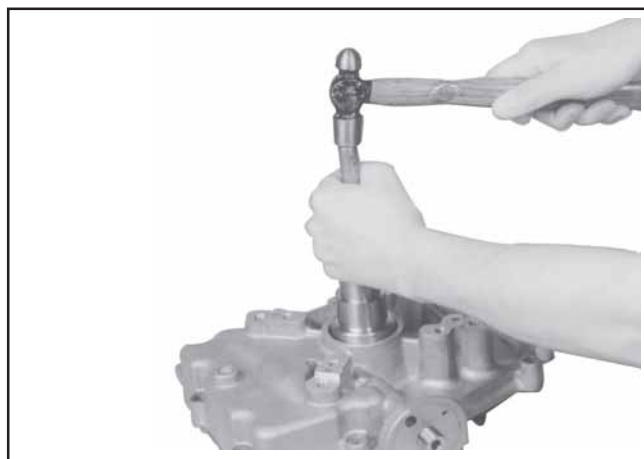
Installazione del paraolio nella coppa dell'olio.
